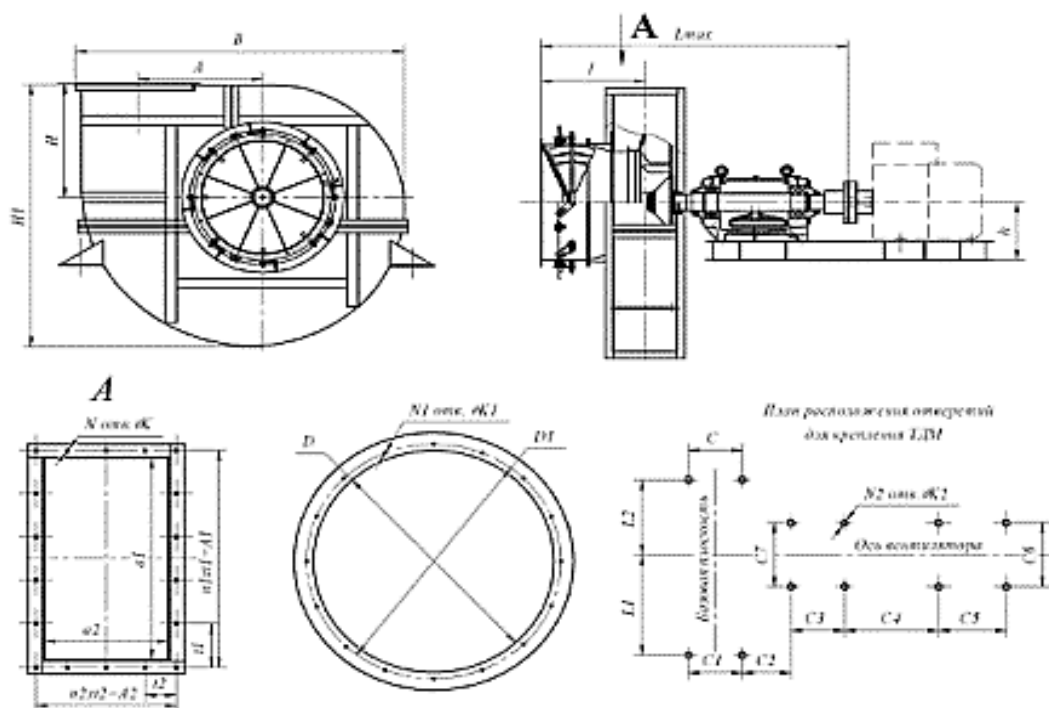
Габаритный чертёж дутьевых вентиляторов
